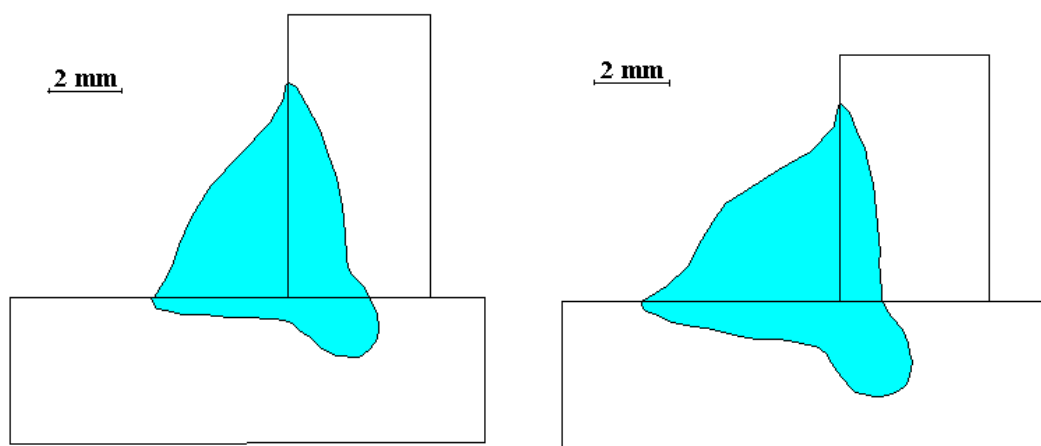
Geometrie makrostruktury vzorku X4c003
